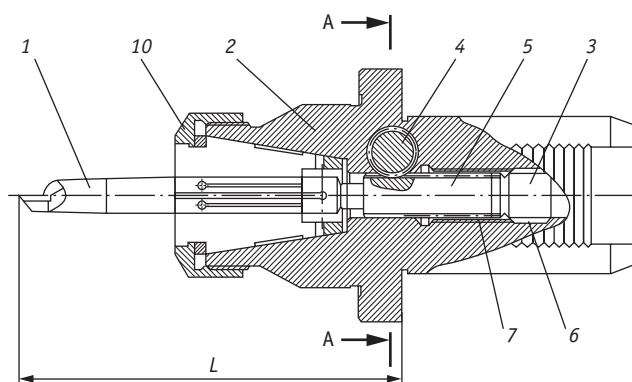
Устройство для осуществления осевой регулировки вылета расточного резца
